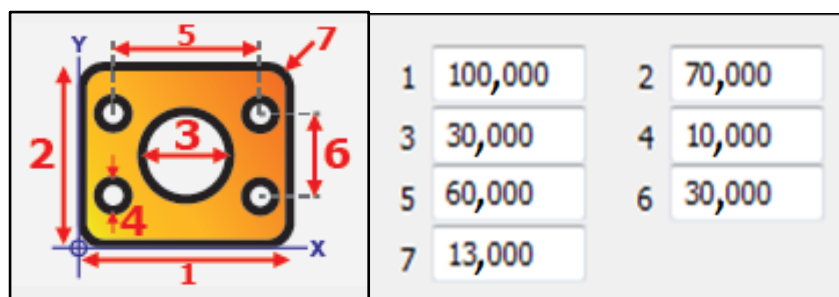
Parámetros del diseño, en milímetros, de la pieza A en programa BobCAD – CAM
